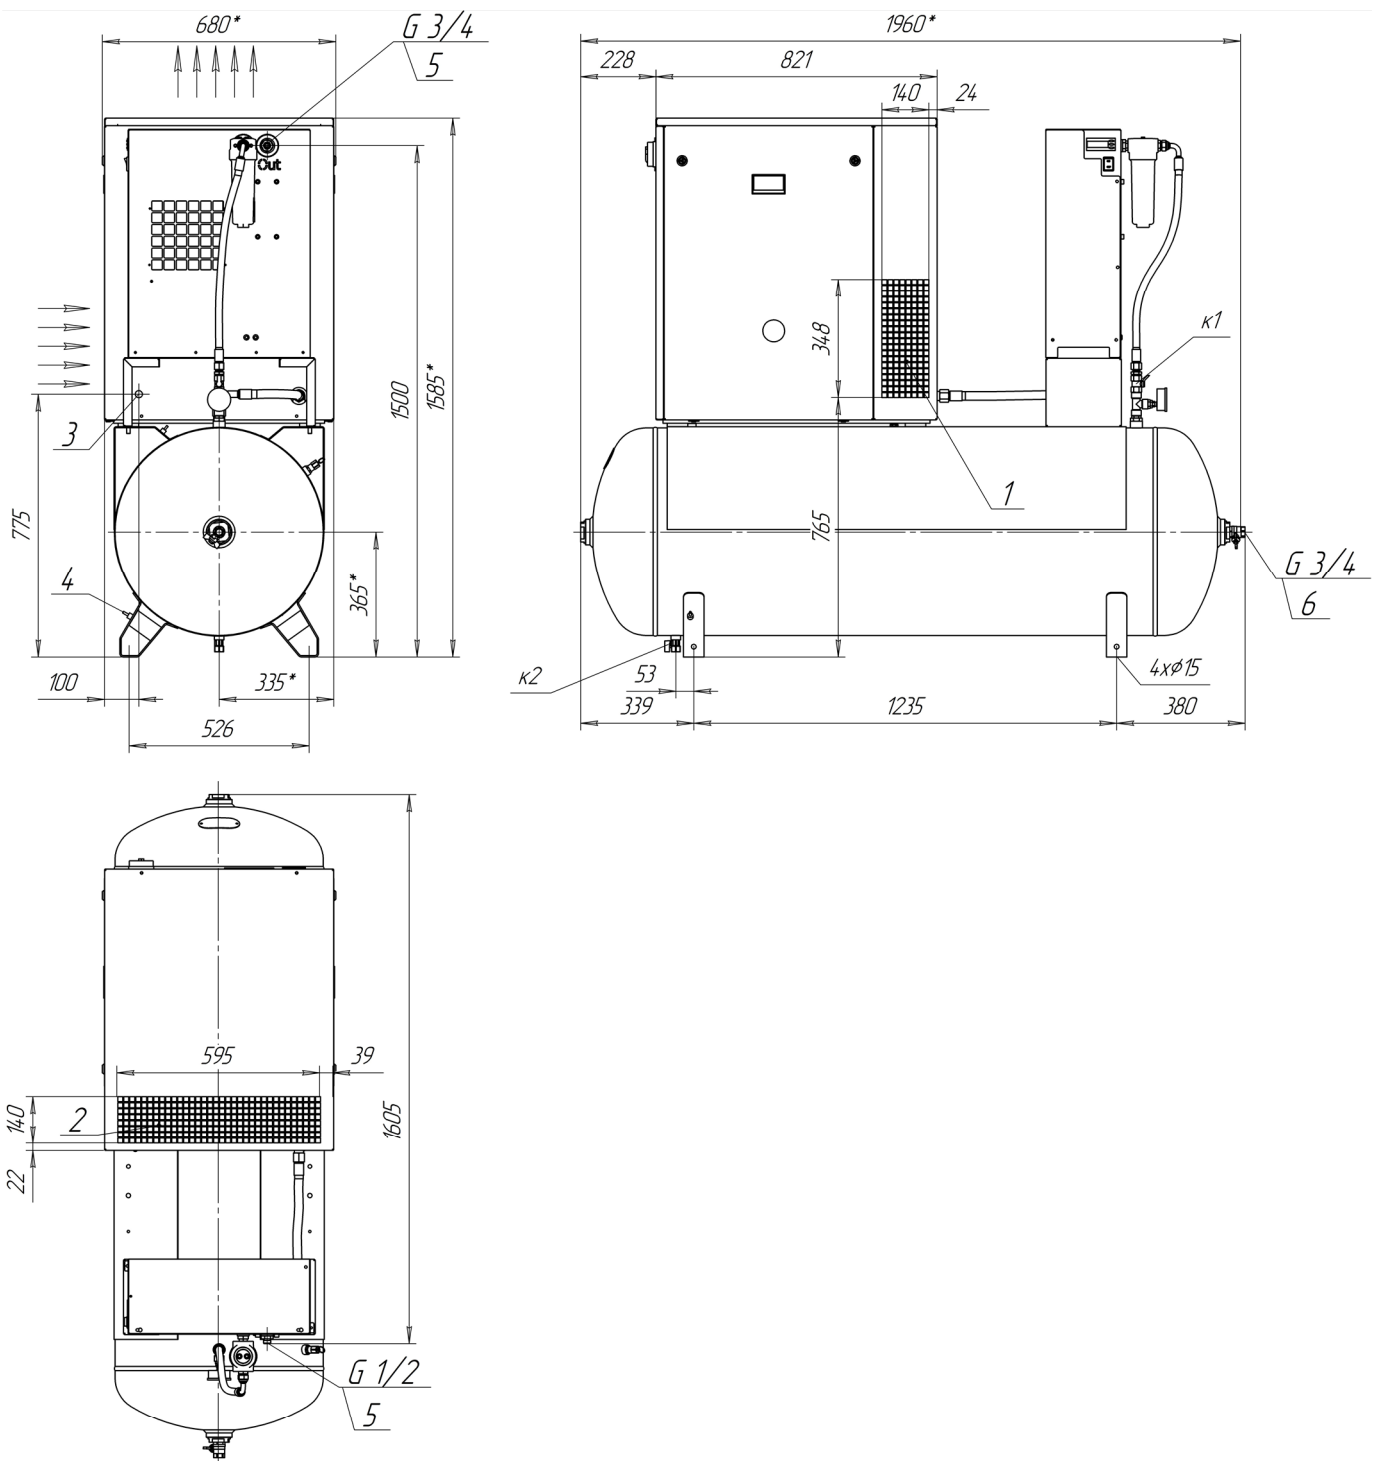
Присоединительные и установочные размеры компрессорной установки ВК5Е-..., ВК7Е-..., ВК10Е-...
